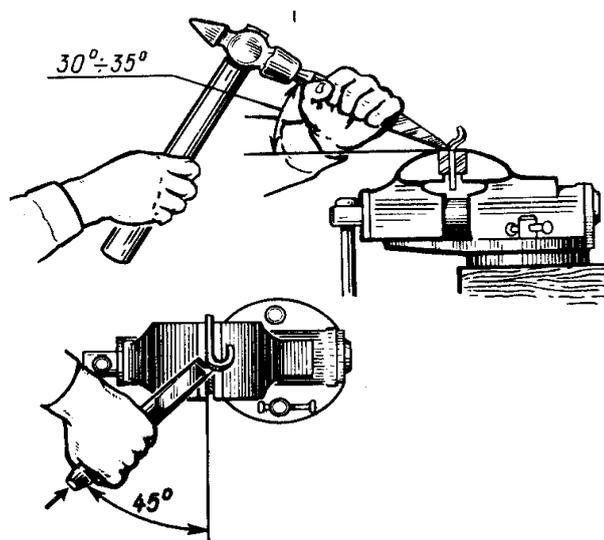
Углы наклона зубила по отношению к оси губок тисков и обрабатываемой поверхности заготовки
